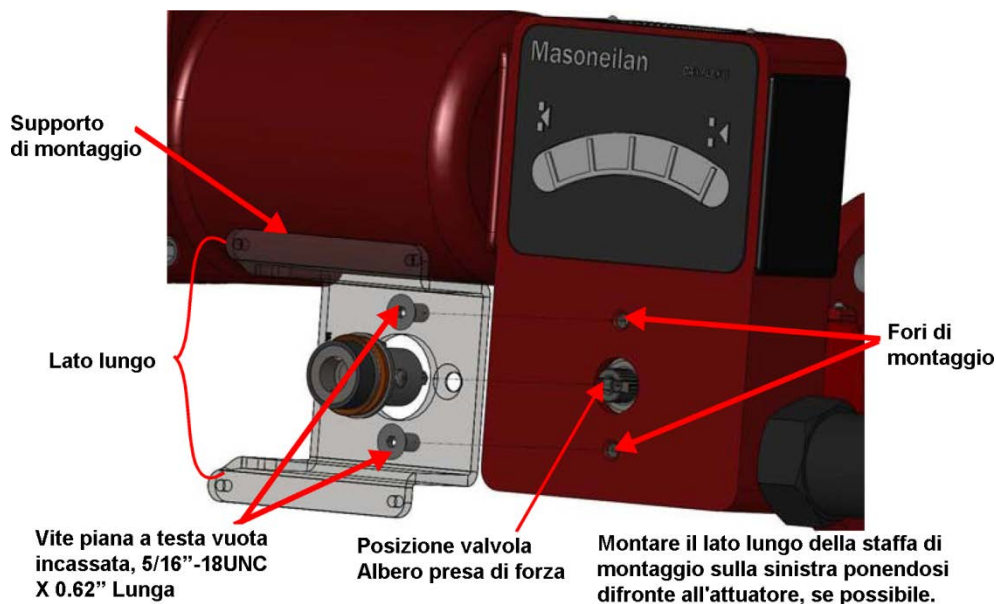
Camflex con supporto di montaggio (vista laterale)
